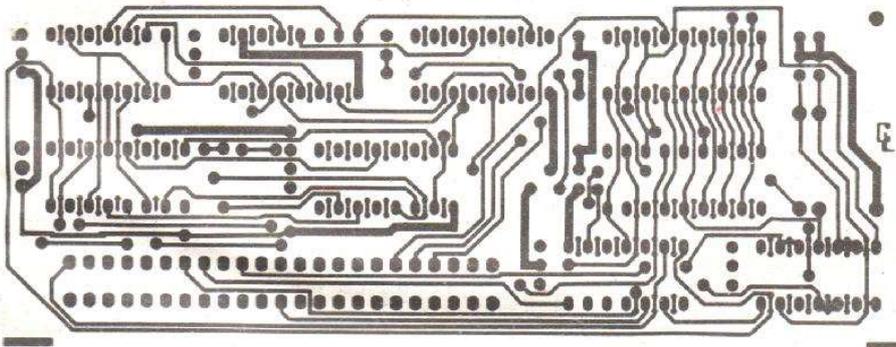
Dessin du circuit imprimé, côté composants, échelle 1.
